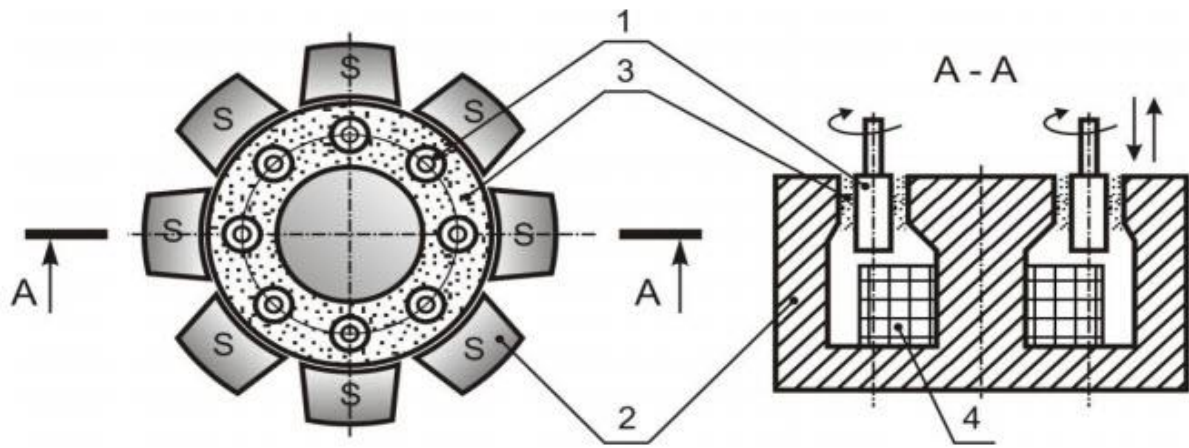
Схема установки типу «кільцева ванна». 1 - заготовка, 2 – полюсні наконечники, 3 - магнітно-абразивний порошок, 4 - котушка електромагніта
